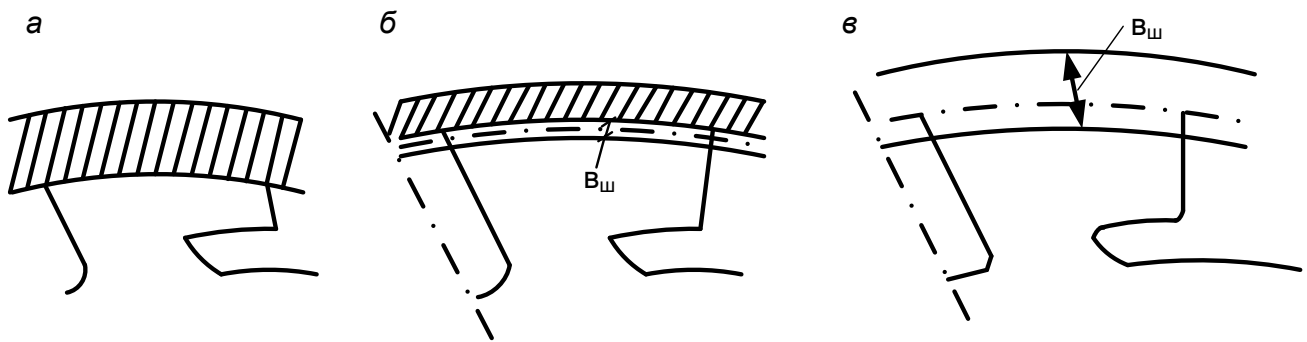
Способы выполнения остова тягового двигателя: а – массивный (литой) остов; б – частично шихтованный остов; в – шихтованный остов
